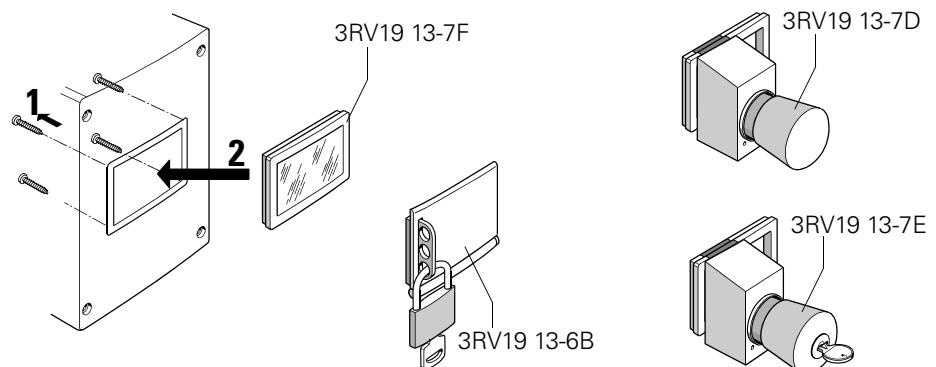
Zubehör für Gehäuse und Frontplatten (Baugröße S00)
